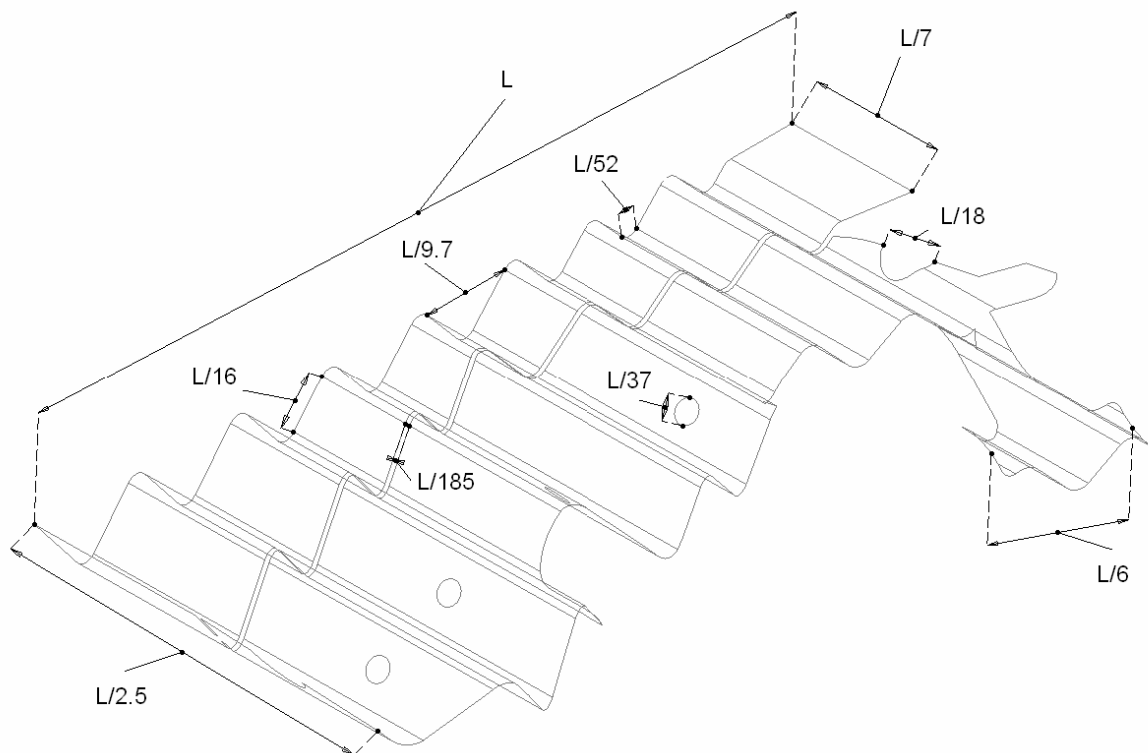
Forme de la pièce et données dimensionnelles en vue isométrique.
